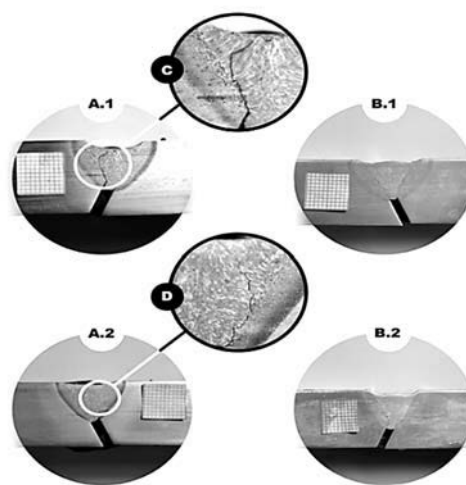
Макрошлифы технологической пробы Тэккен: А – сварка с использованием традиционной защитной газовой смеси (Ar + CO_2); В – сварка с введением в состав защитной газовой смеси SF_6 ; С, D – трещина в сварном соединении технологической пробы
